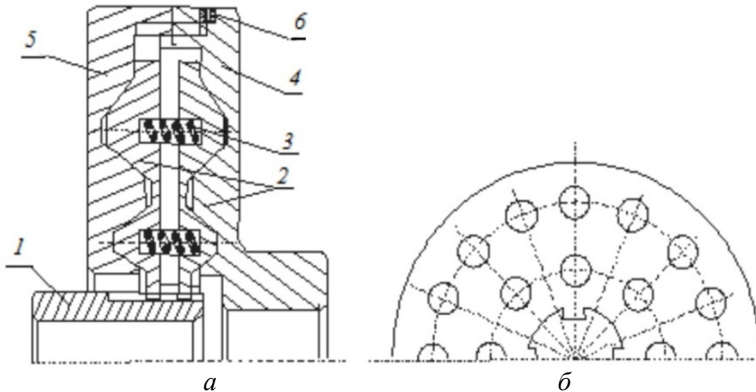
Принципова конструкція фрикційної муфти: а – осовий розріз; б – вигляд на внутрішню поверхню проміжного диску
